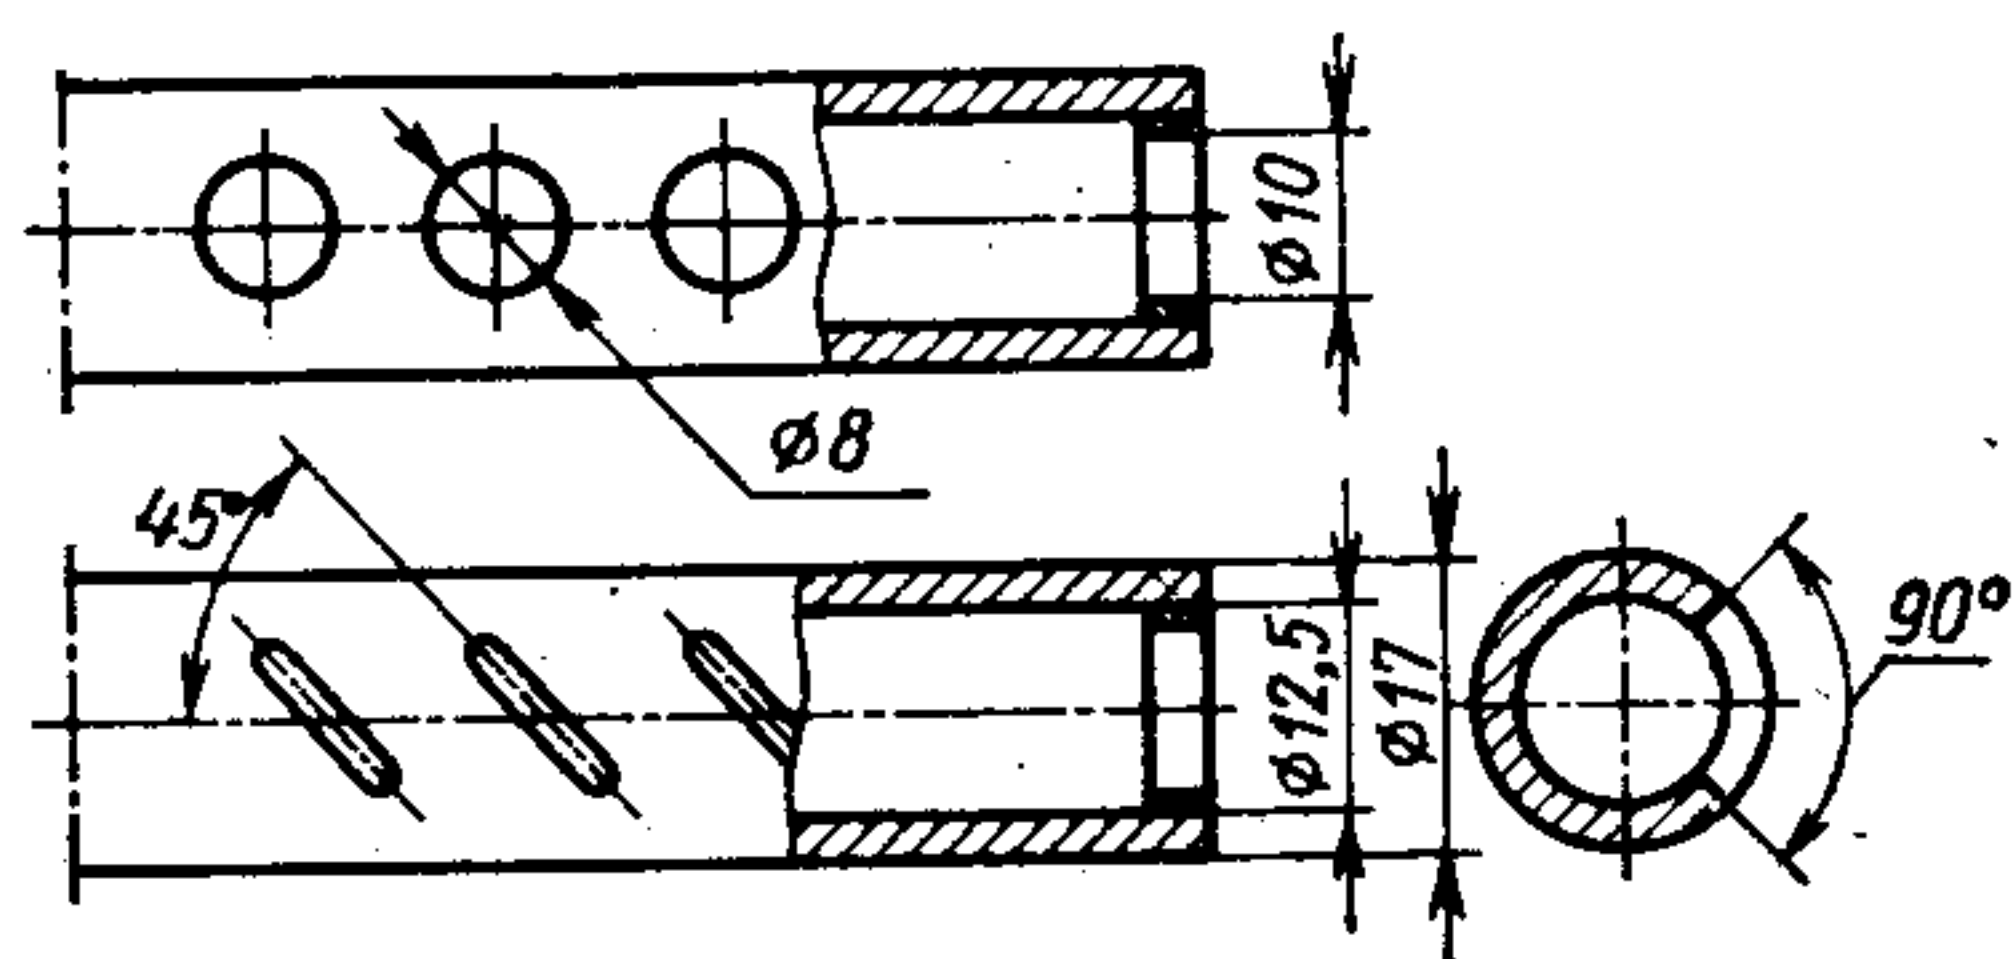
Брызгальные трубки для подачи смазки в подшипник
